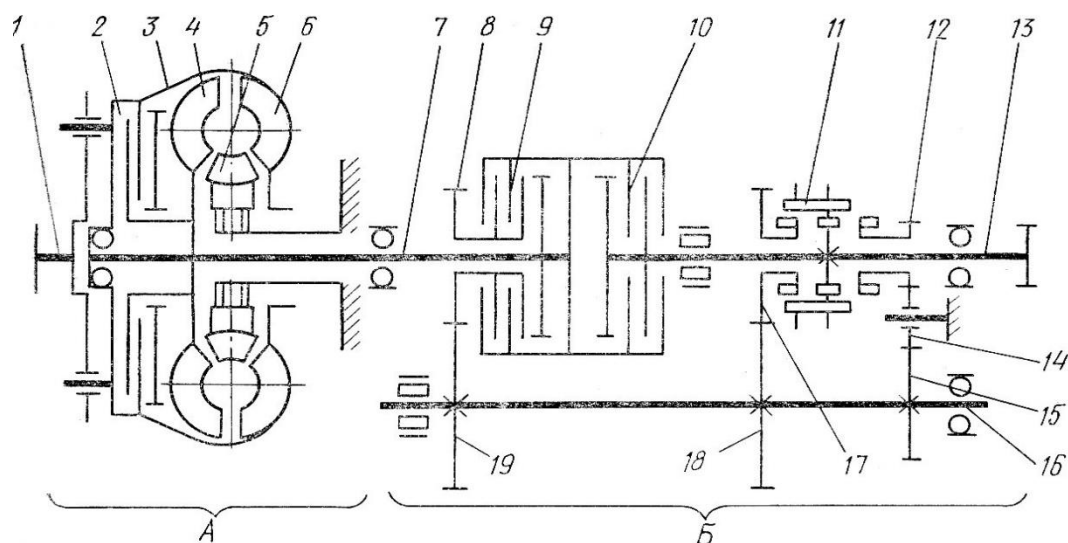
Схема гидромеханической коробки передач: 1 – ведущий вал; 2 – блокирующее устройство; 3 – корпус; 4 – турбинное колесо; 5 – реактор; 6 – насосное колесо; 7 – первичный вал; 8,17,18,19 – шестерни; 9,10 – диски фрикционной муфты; 11 – зубчатая муфта; 12,14,15 – шестерни заднего хода; 13 – вторичный вал; 16 – промежуточный вал
